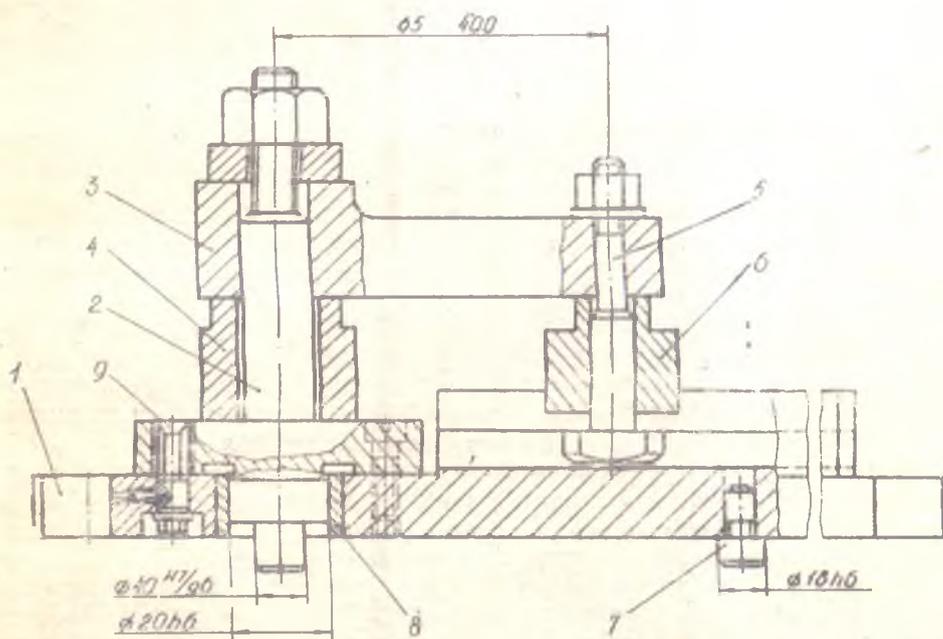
Переналаживаемое приспособление для обработки контуров заготовок
